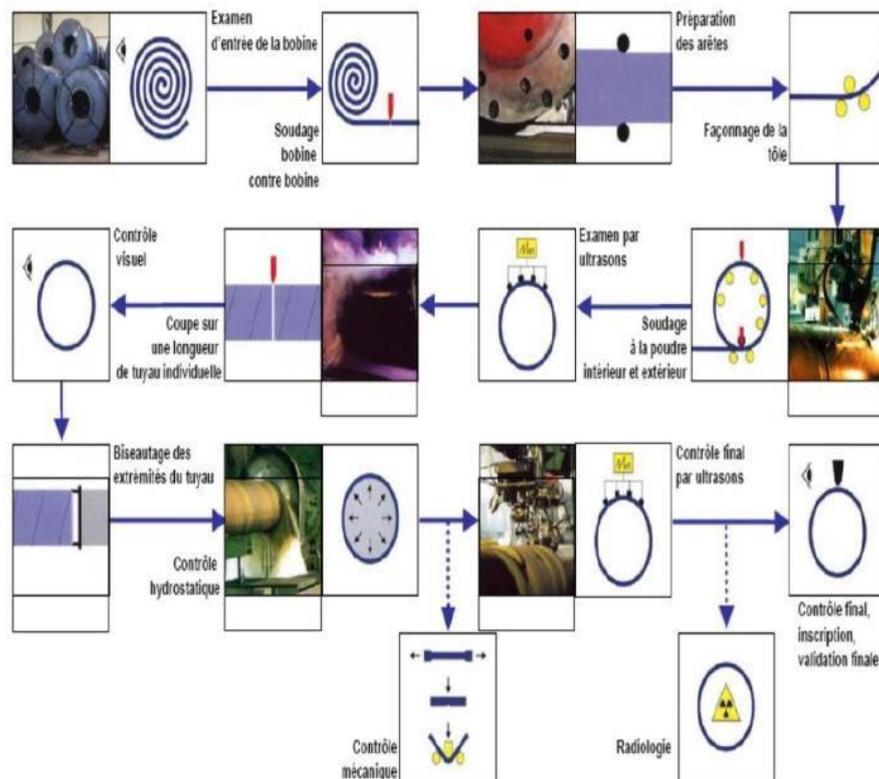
Chaîne de fabrication du tube soudé en spirale.
